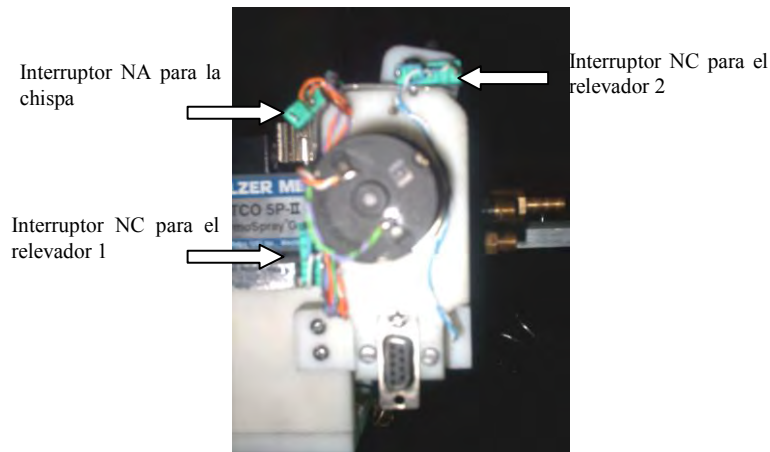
Acoplamiento del motoreductor a la carcasa de automatización
